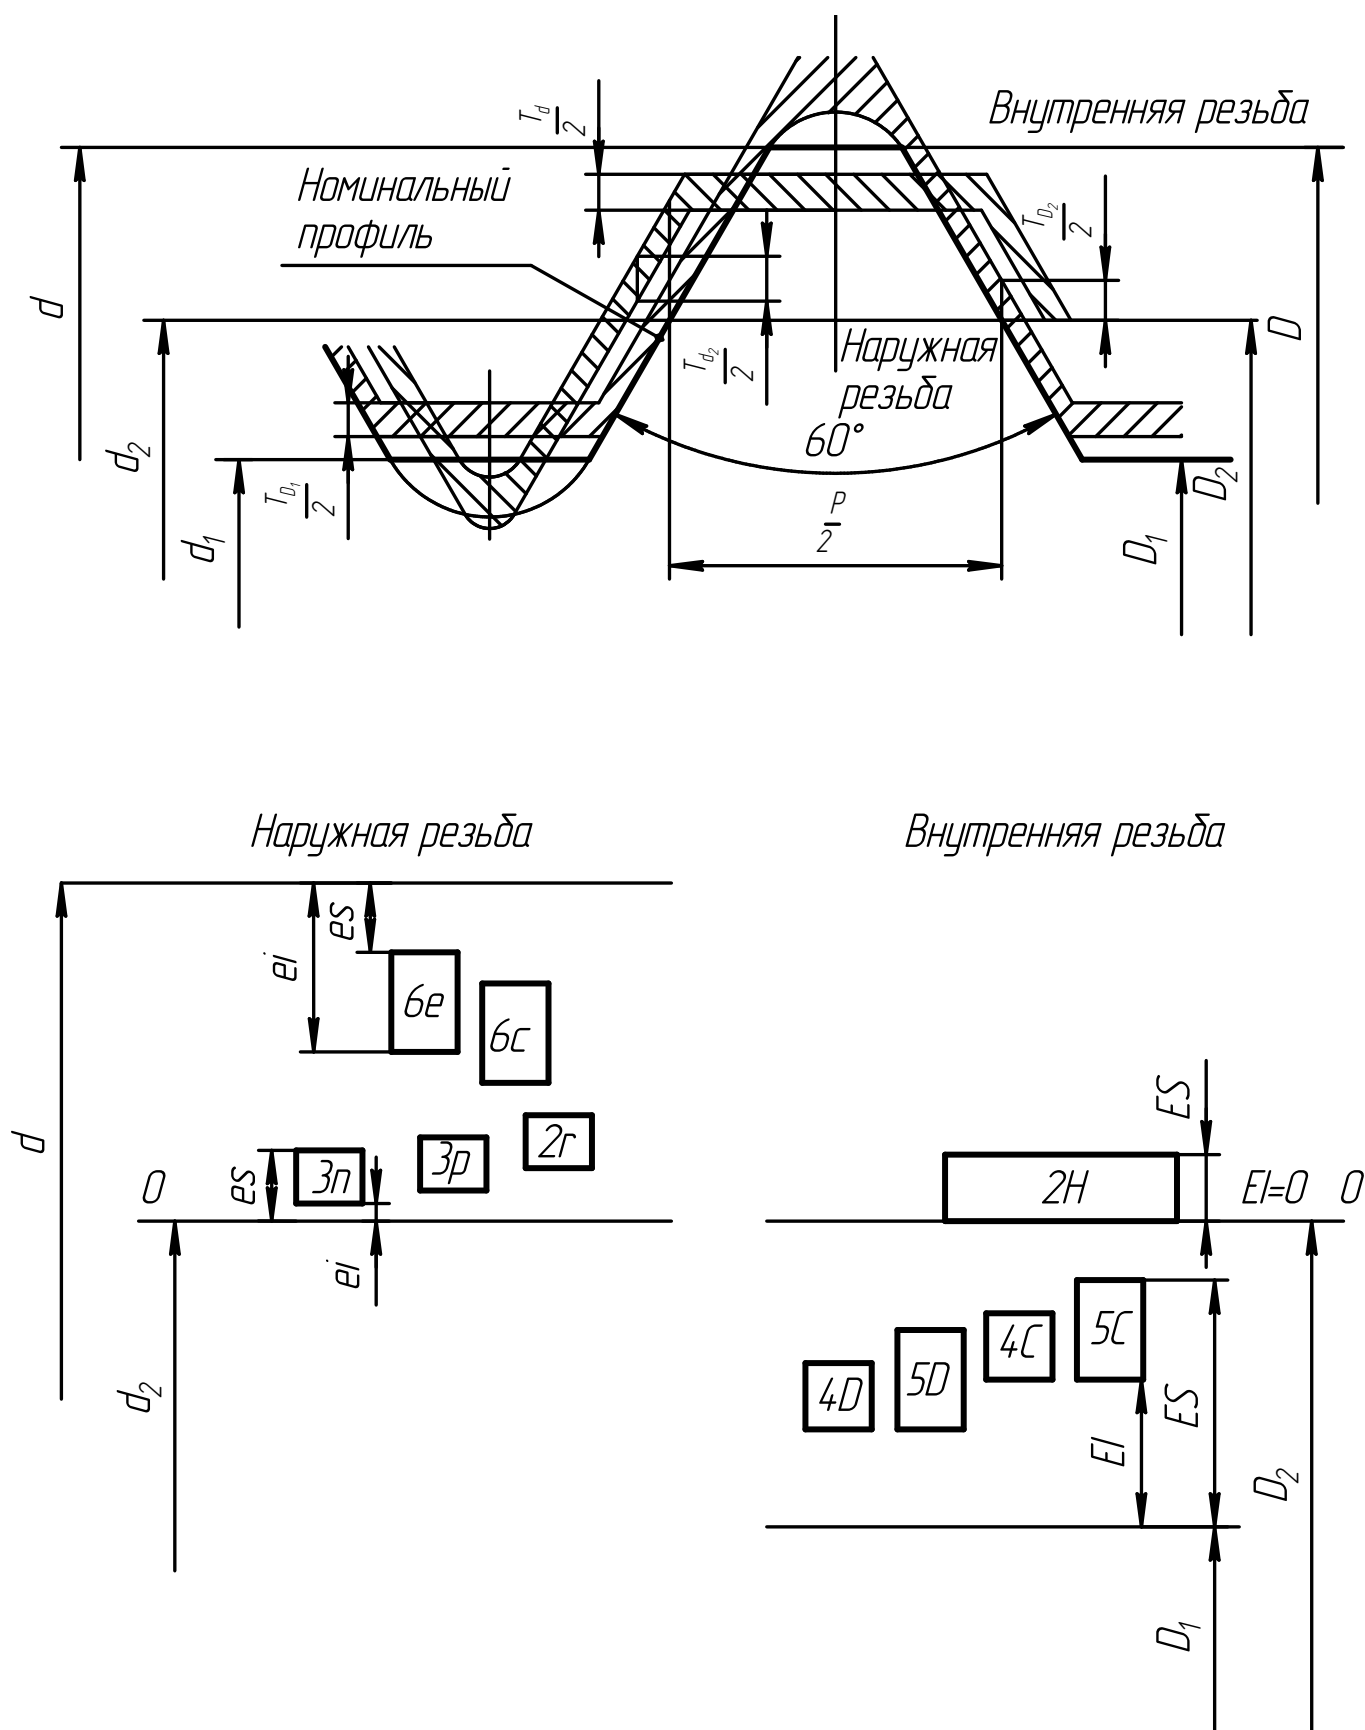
Расположение полей допусков резьбы с натягом
